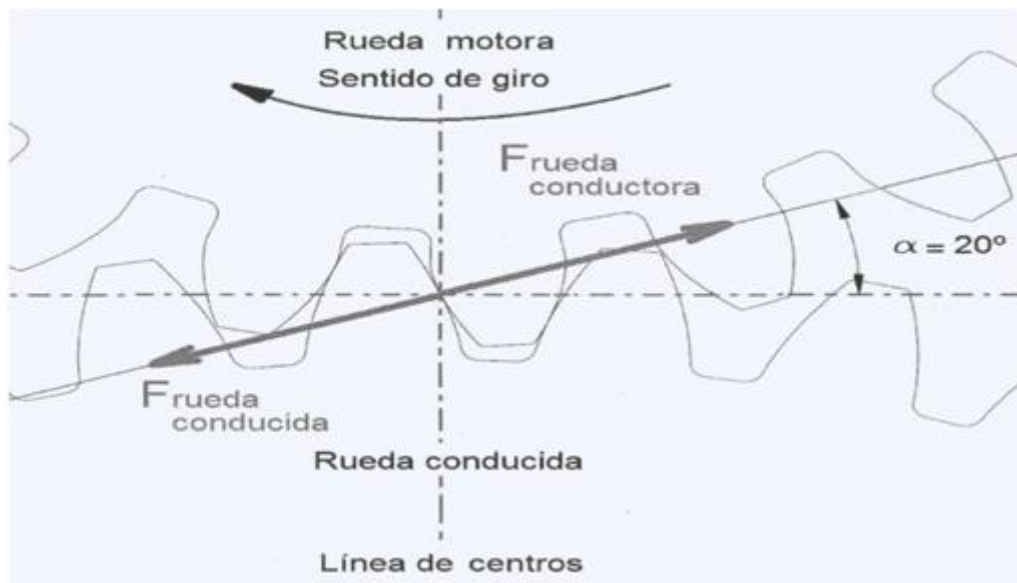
Fuerza resultante en contacto entre dientes de los engranajes
